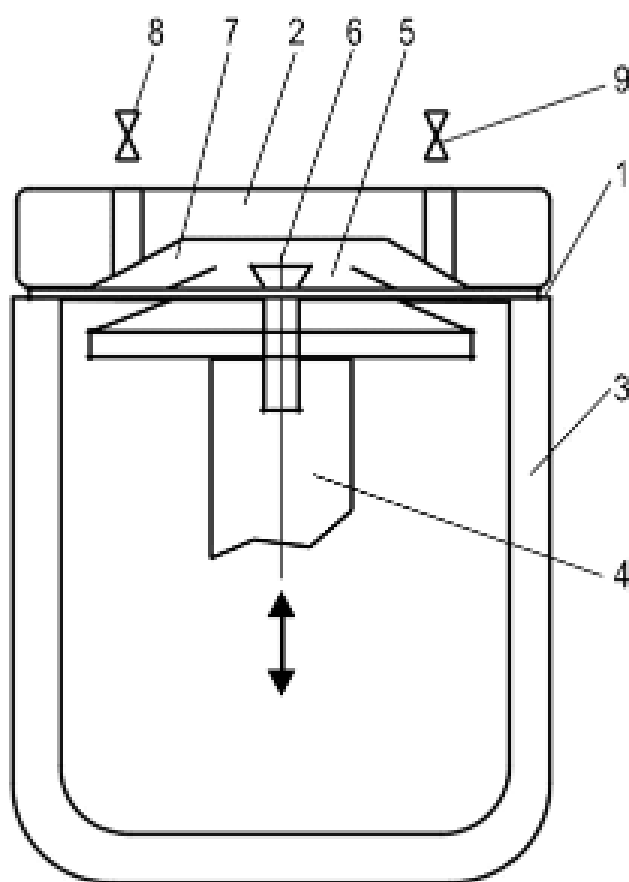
Принципиальная конструкция мембранных насосов. 1 – эластичная диафрагма; 2 – головка; 3 – корпус; 4 – шатун; 5 – грибовый толкатель; 6 – винт; 7 – вакуумная камера; 8 – всасывающий клапан; 9 – выхлопной клапан
